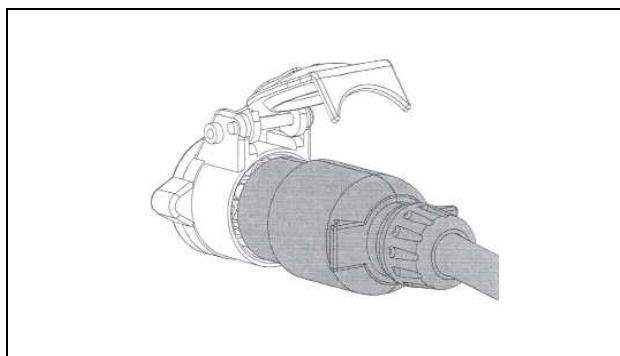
INSTALACJA HYDRAULICZNA PRASY
